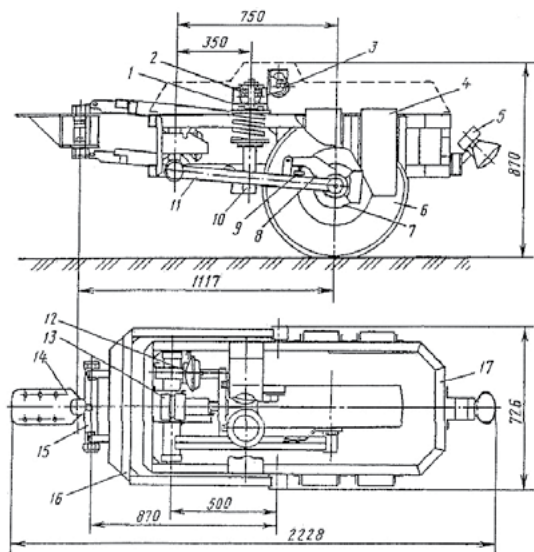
Конструкция тестера ШТ-1: 1 — опорное устройство; 2 — датчик силы (ДС-6); 3 — лебёдка; 4 — балластные грузы; 5 — датчик скорости движения; 6 — измерительное колесо; 7 — дисковый тормоз; 8 — рычаг; 9 — датчик тормозного момента; 10 — амортизационные стойки; 11 — продольный рычаг; 12 — пневмогидравлический усилитель; 13 — контроллер; 14 — буксирное устройство; 15 — переходное звено; 16 — реактивные штанги; 17 — объёмная рама
